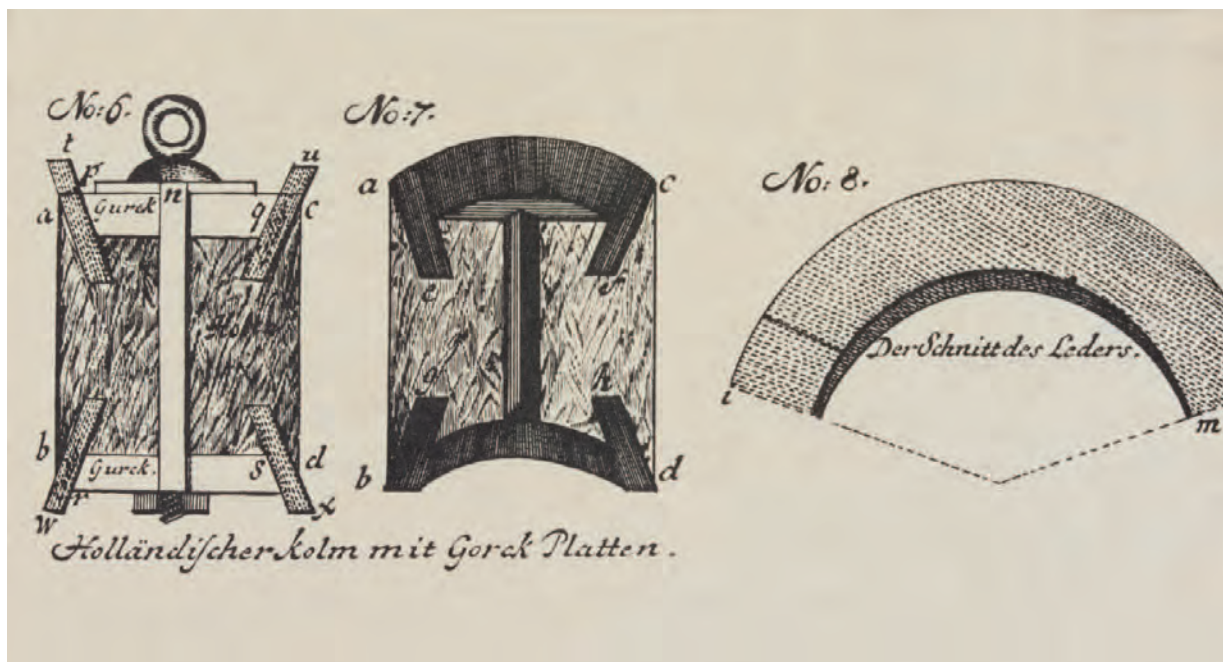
Jakob Leupold, *Theatrum Machinarum Hydraulicarum*: Holländischer Kolm, 1724/25
